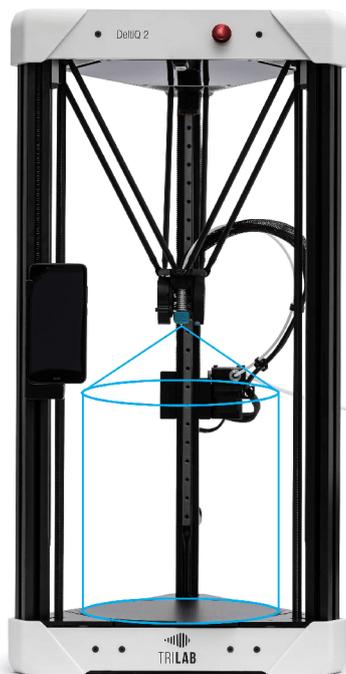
a) TriLab DeltiQ2 s extruderem Titan
